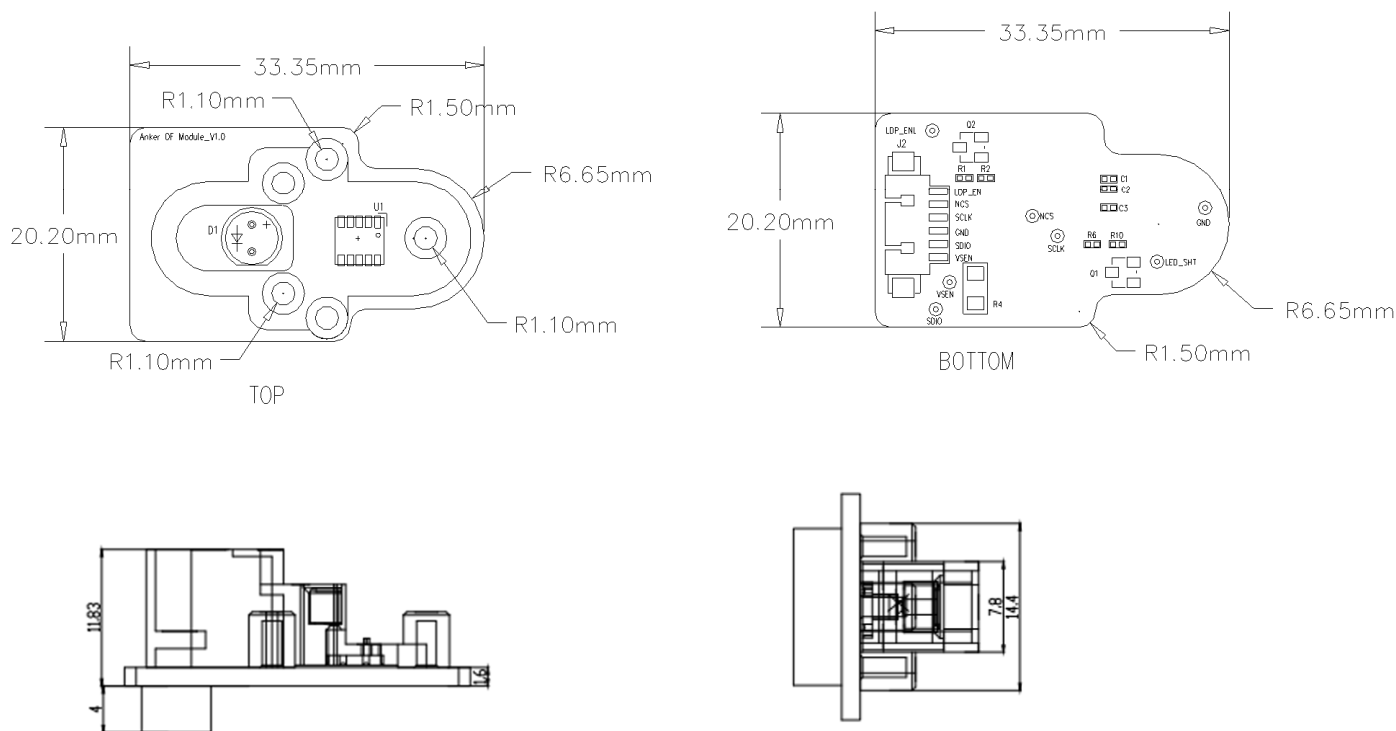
模组PCB尺寸 单位：mm 公差：+0.1mm
